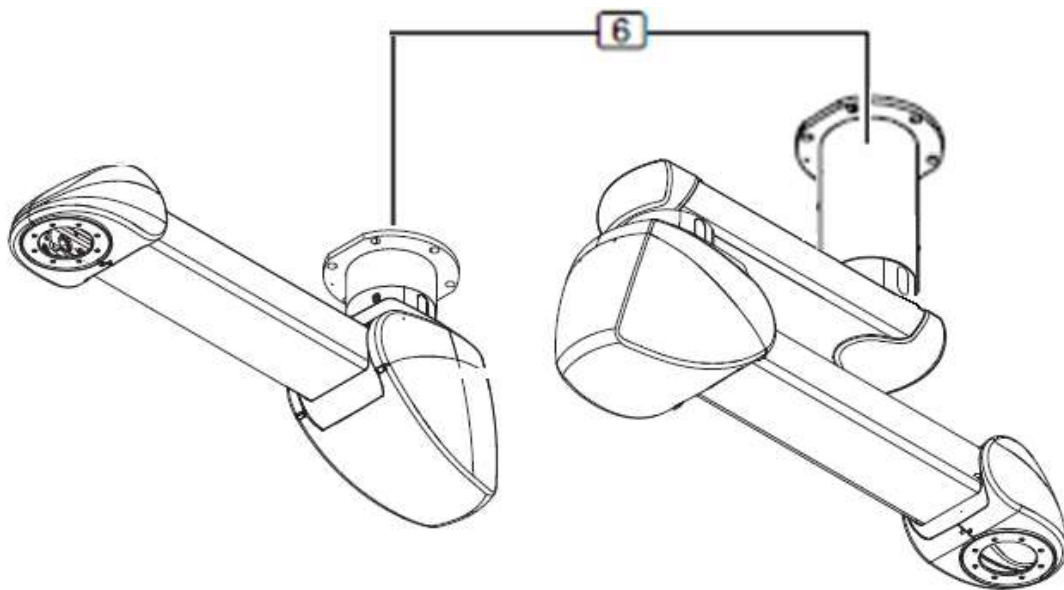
Montage von COLUMN AIR mit Doppelarm und COLUMN AIR mit Einzelarm
